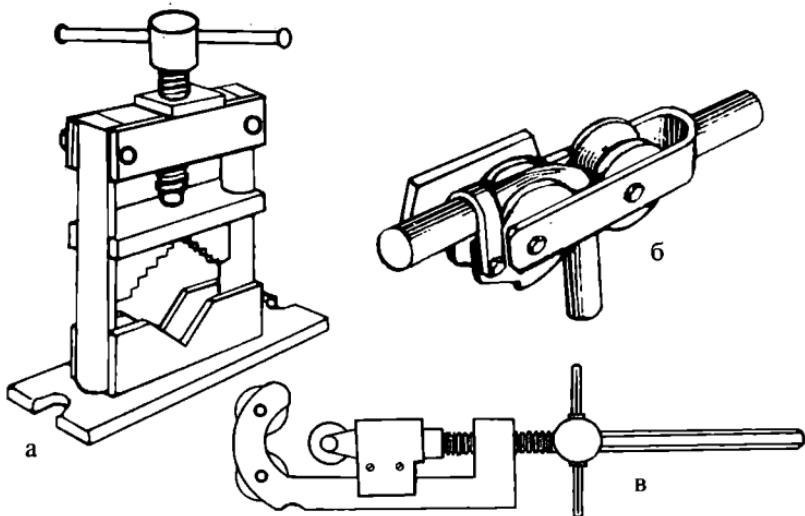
Инструменты для работ с трубами: а — прижим; б — стационарный трубогиб Вольнова; в — труборез
